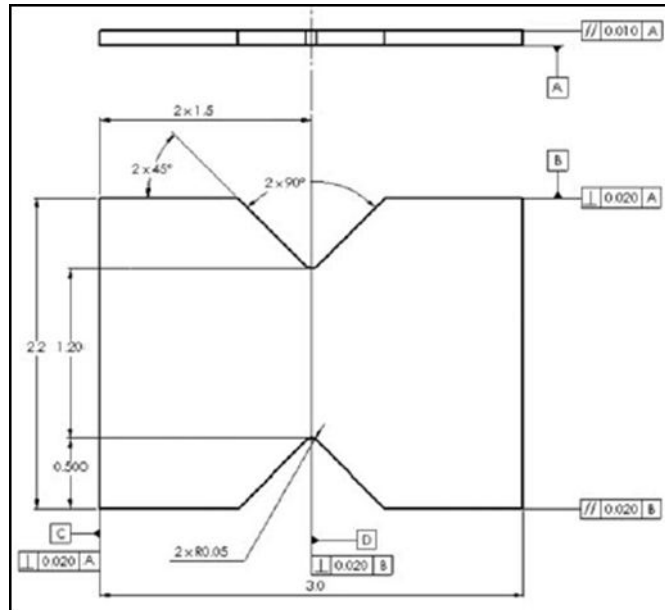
Geometria do corpo de prova do ensaio cisalhamento no plano v-notched rail (dimensões em mm) [ASTM D7078].
